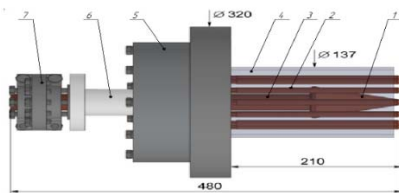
Газоразрядный магнитоплазменный компрессор:
